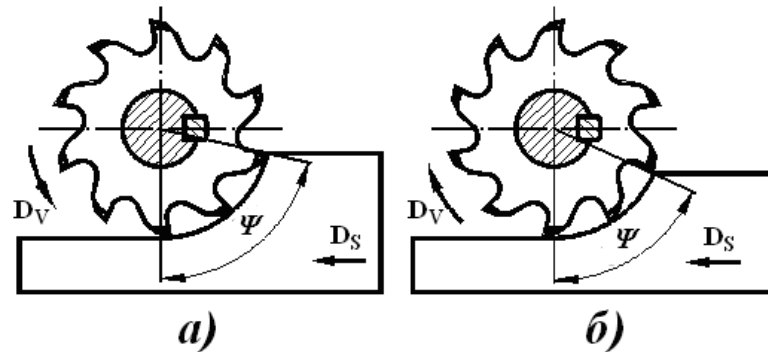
Периферійне або циліндричне фрезерування (циліндровими, дисковими і іншими однотипними конструкціями фрез): а) зустрічне; б) попутне. D_v – головний рух інструменту, D_s – рух подачі; ψ – кут контакту.
